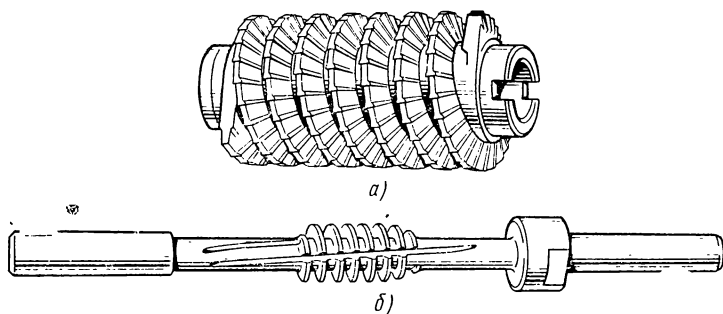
Инструмент для чистового нарезания зубьев червячных колес:
